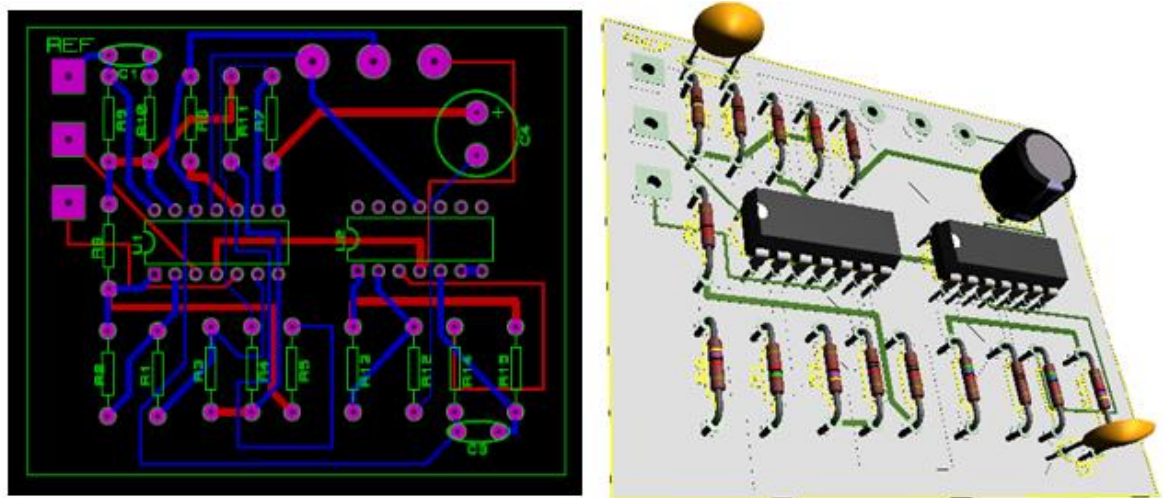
Layout da placa de aquisição de sinais EMG.
